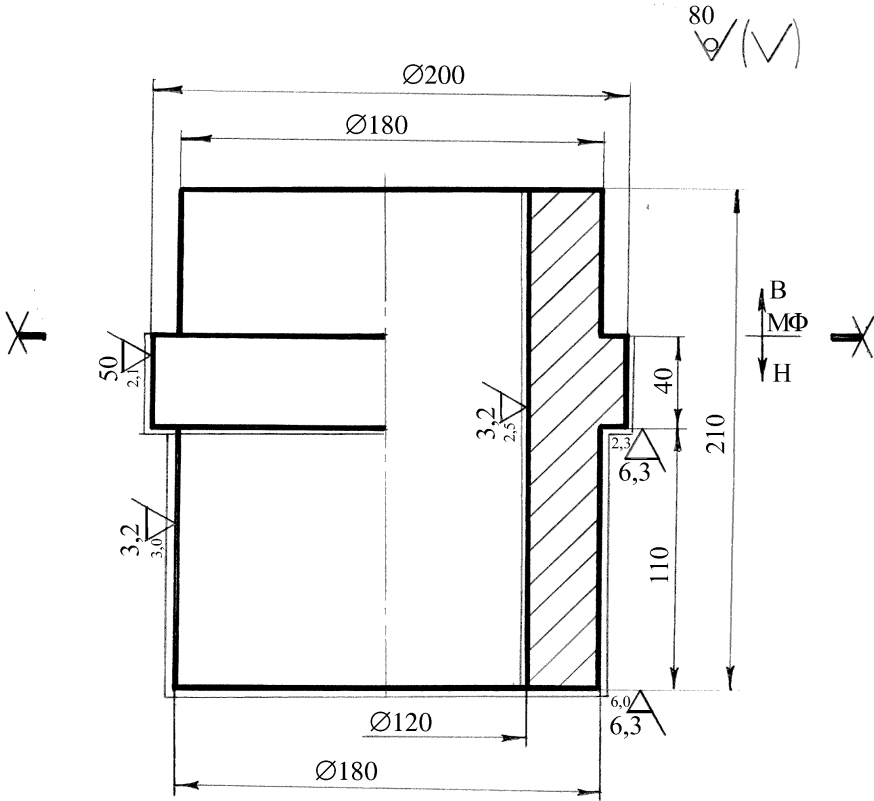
Креслення виливка “Втулка” зі зазначеними припусками на механічну обробку
